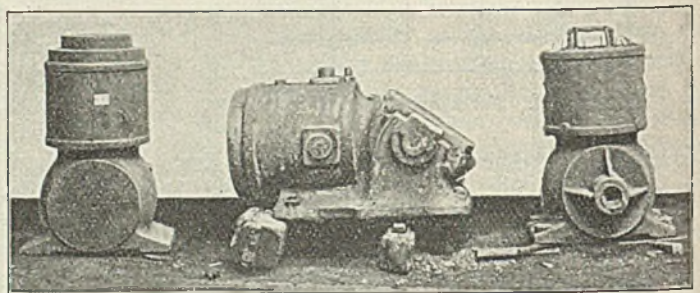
Kompressorenzylinder, gerüttelt auf Maschinen der Badischen Maschinenfabrik.
